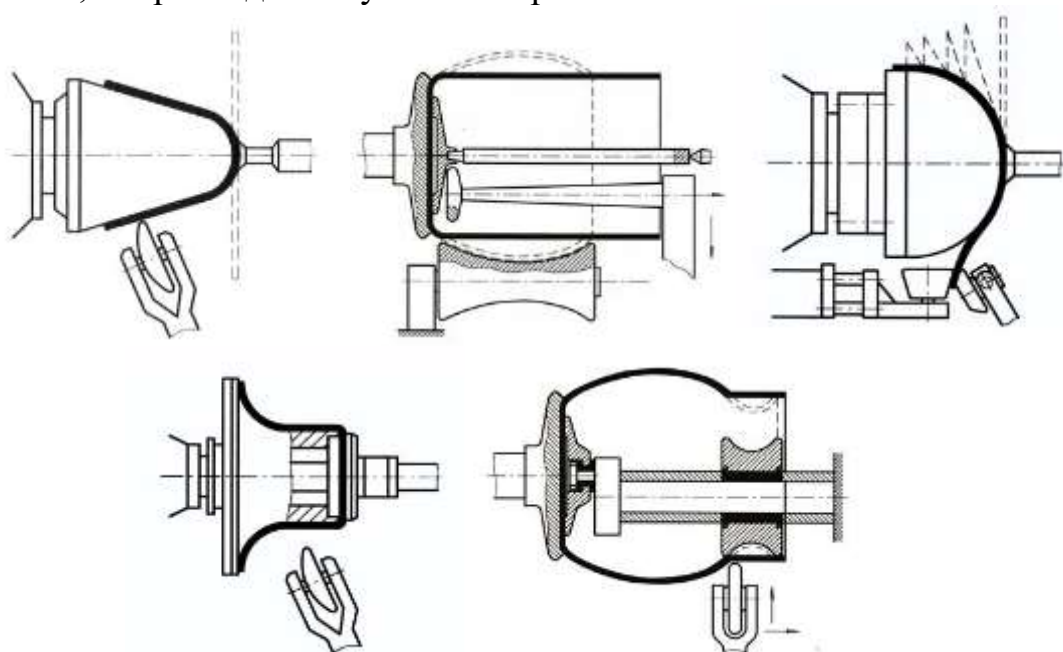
Схеми ротаційного витягування і розкатування
